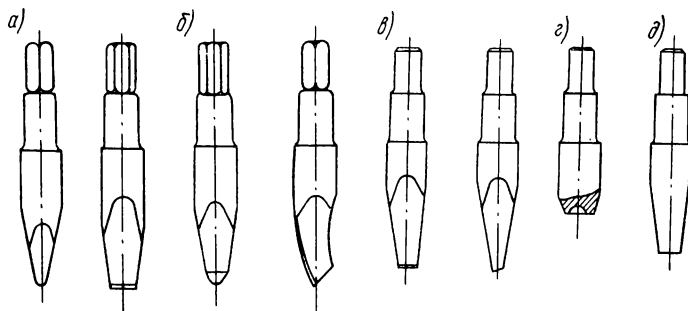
Вставной инструмент для пневматических машин ударного действия: а — зубило; б — крейцмейсель; в — чекан; г — обжимка; д — боек для клепки.
